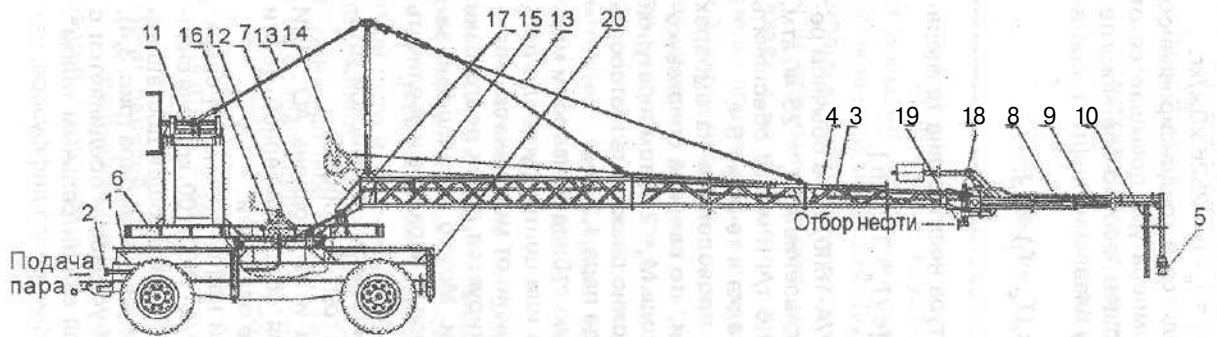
Схема установки для сбора амбарной нефти: 1 - неподвижная платформа; 2 - патрубок для подачи пара; 3, 8, 17 - устройство подачи-отсечки пара; 4 - стрела со сгибом; 5 - насадок; 6 - подвижная платформа; 7 - силовой шарнир; 8 - паропровод; 9 - труба для отбора нефти; 10 - нефтеотборник; 11, 12, 14 - поворотно-подъемные механизмы; 13, 15 - гибкий трос; 16 - вращающиеся парокolleкторы; 19 - патрубок для отбора нефти; 20 - опора платформы
